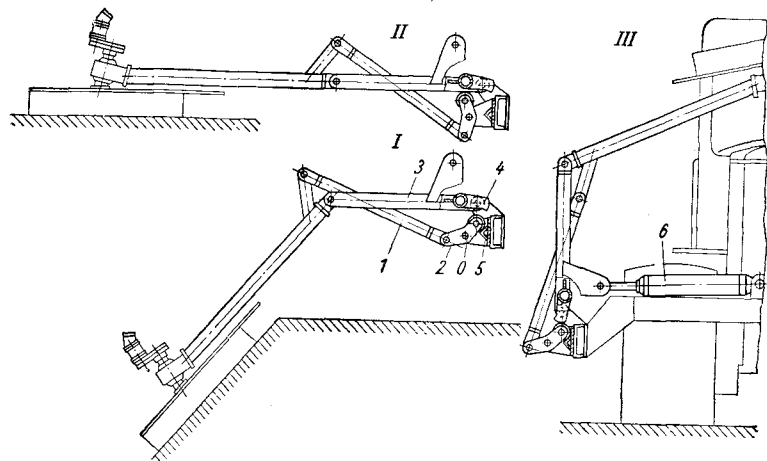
Схема механизма навески каналоочистителя-косилки МСР-1,2 без применения гидроцилиндра поворота рамы рабочего органа:
